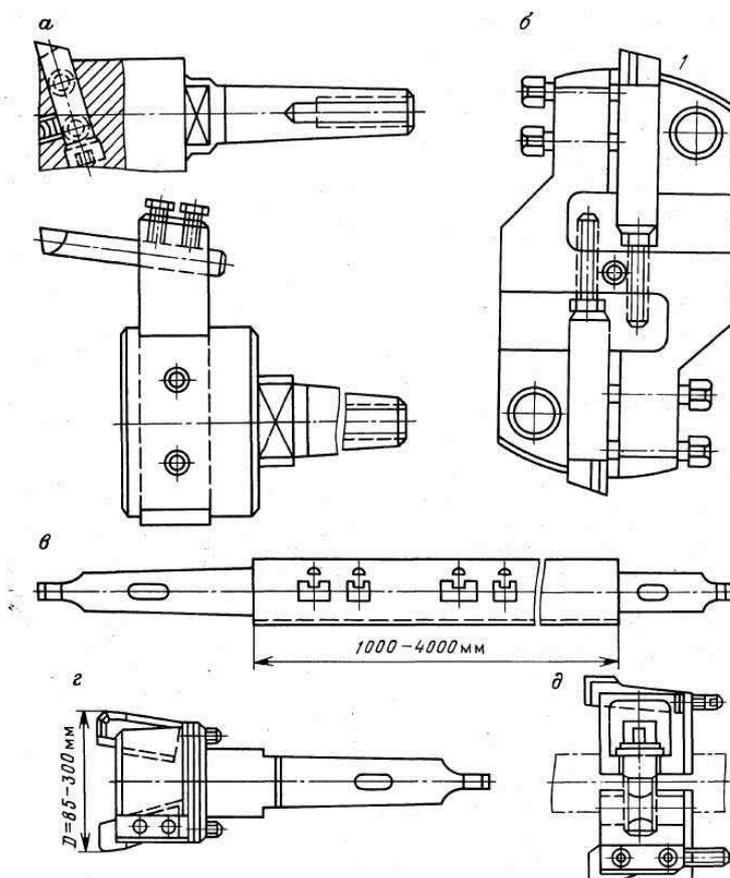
Инструмент, применяемый для растачивания отверстий: а - расточные оправки для отверстий среднего диаметра; б - расточная оправка для отверстий большого диаметра; в - борштанга; г - концевая двухрезцовая расточная головка; д - разъемный расточной блок
